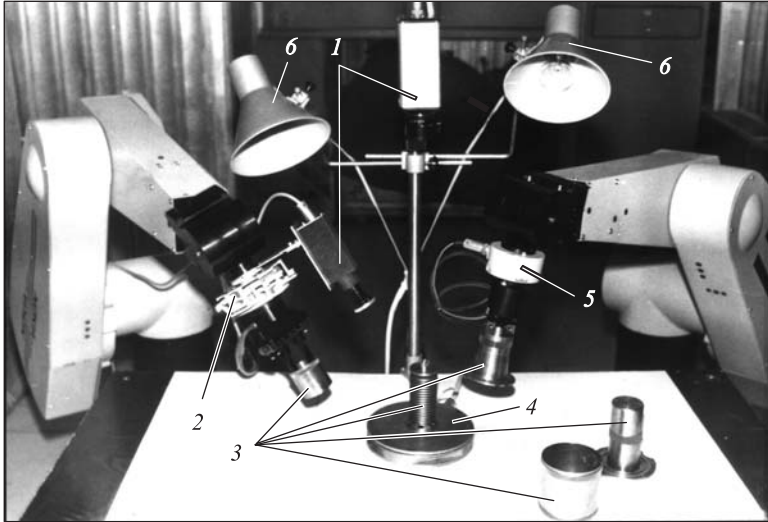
Адаптивный сборочный комплекс с роботами РМ-01:
